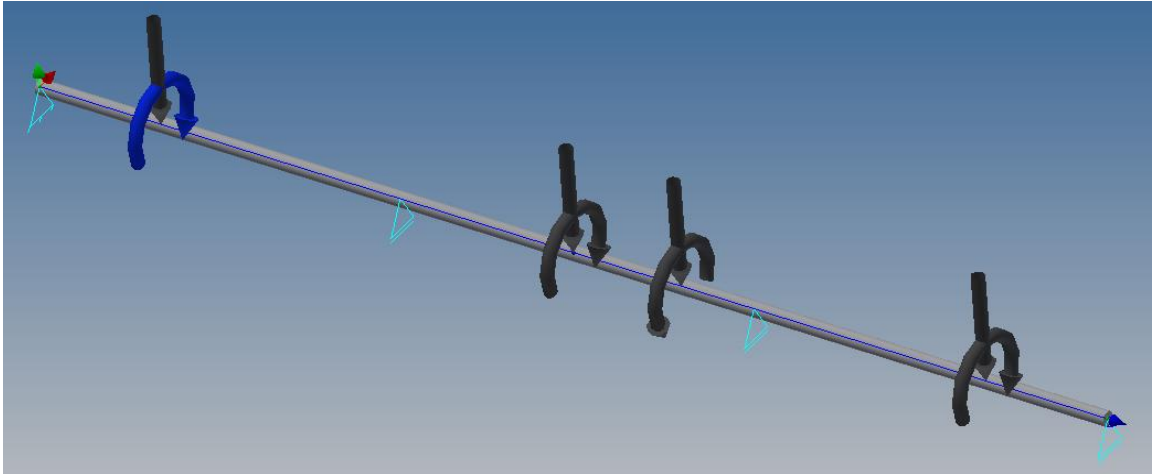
Diseño del eje en CAD Inventor Profesional.
